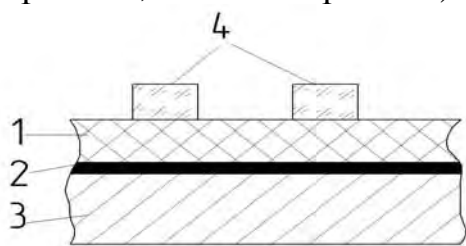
Крепление детали действием сил капиллярного натяжения
